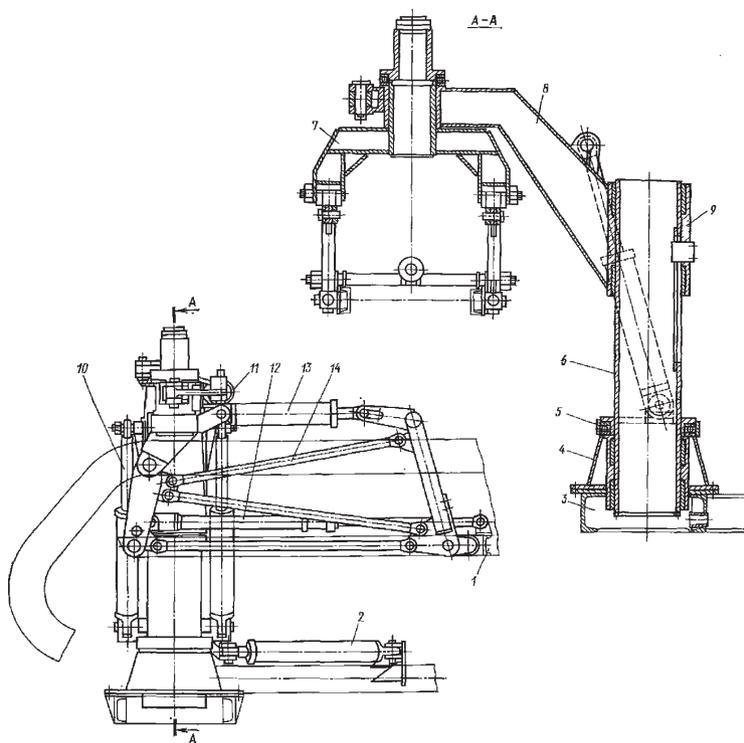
Навеска рабочего органа каналоочистителя МР-15: 1 — рабочий орган; 2 — гидроцилиндр поворота колонны; 11 — гидроцилиндр поворота рабочего органа, 10 — гидроцилиндр подъема рабочего органа, 12 — гидроцилиндр выдвижения рабочего органа, 13 — гидроцилиндр наклона рабочего органа: 3 — рама каналоочистителя; 4 — основание; 5 — подшипник; 6 — колонна; 7 — портал; 8 — кронштейн; 9 — ползун; 14 — подвеска.
